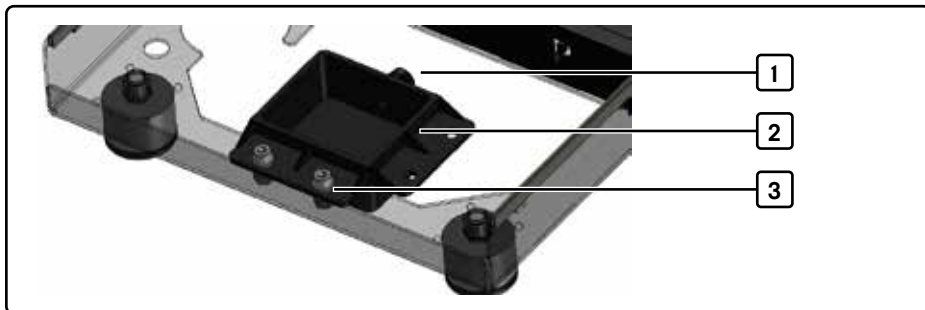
Rückansicht mit Drehventil und Wasseranschlusstutzen
